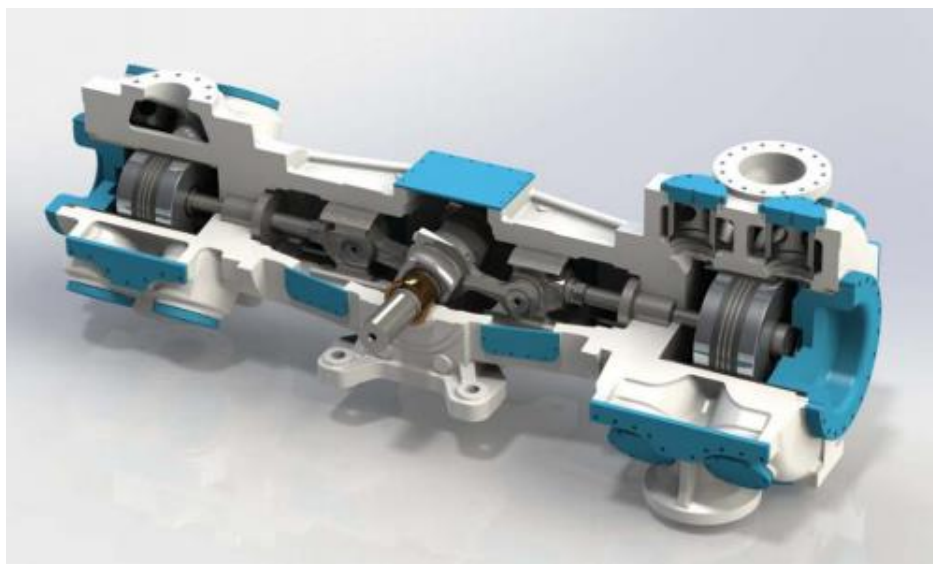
оппозитный горизонтальный компрессор ДКУ-3-01.000
